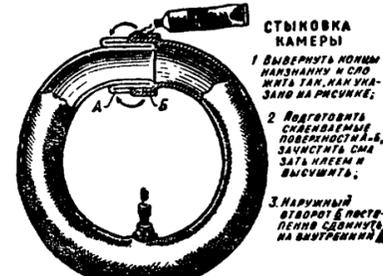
Изготовление камеры малого размера из велосипедной камеры путем склейки в стык
